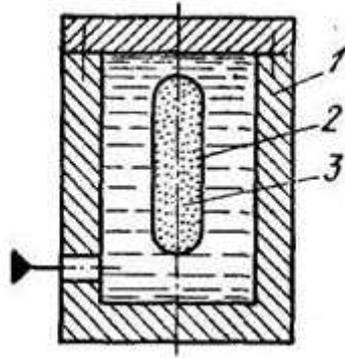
Схема изостатического прессования: 1- камера, 2- прессовка, 3- металлический порошок
